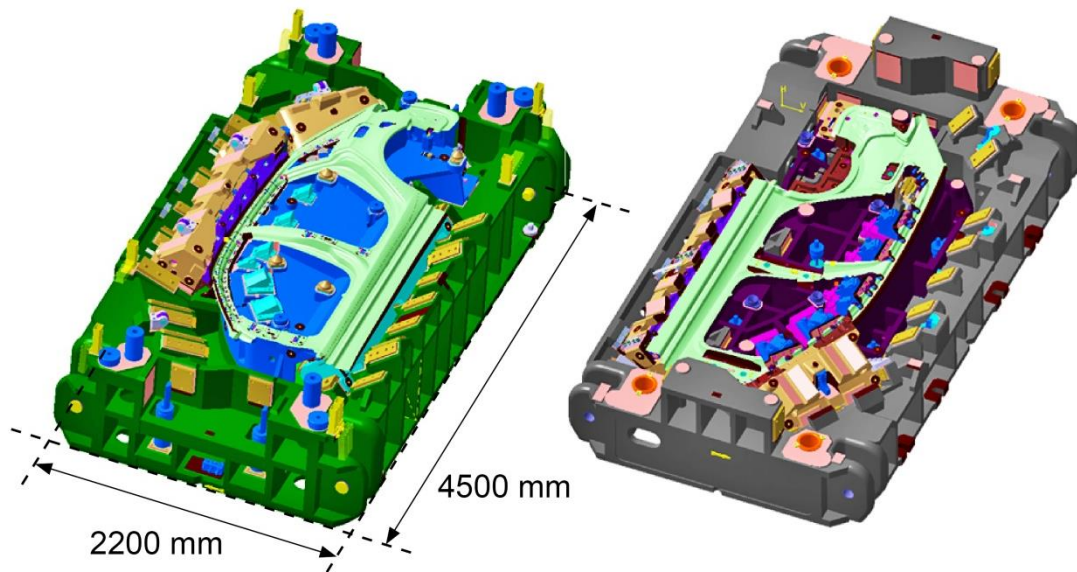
Seitenwandrahmen Werkzeug AUDI A3 Sportback OP50: links Werkzeugunterteil, rechts Werkzeugoberteil
